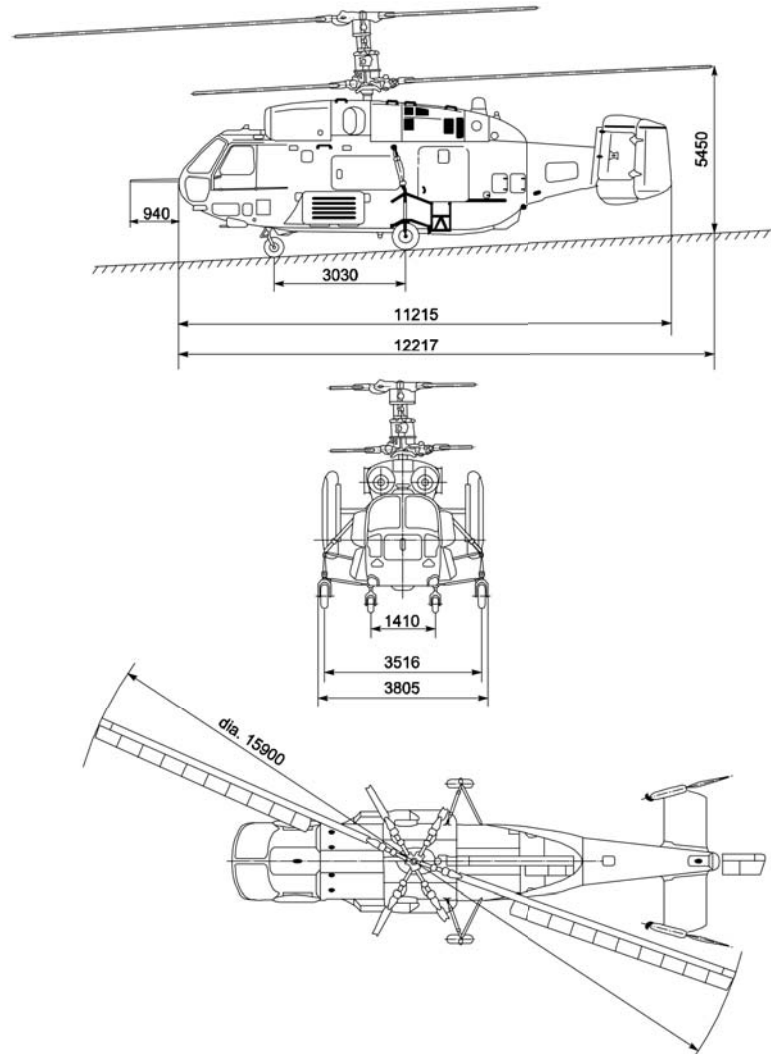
Dimensões principais do Helicóptero Kamov Ka-32 [75].
